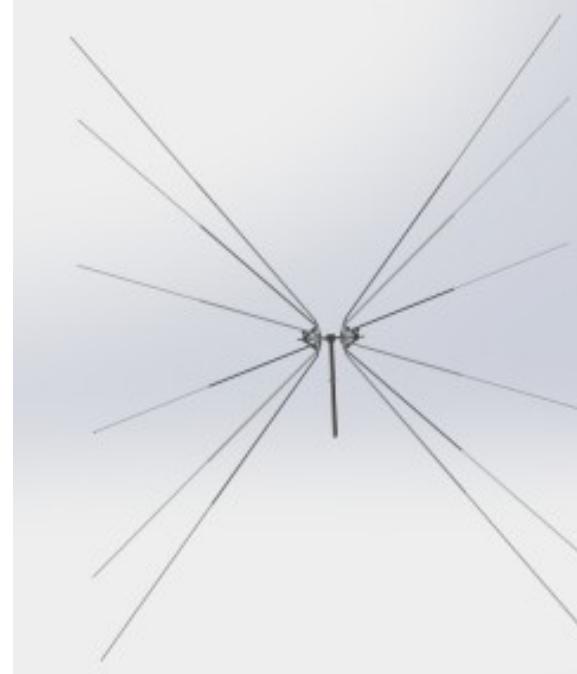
Balun + BBFA 9146 Elemente mit großem Öffnungswinkel und mit Extensions.
